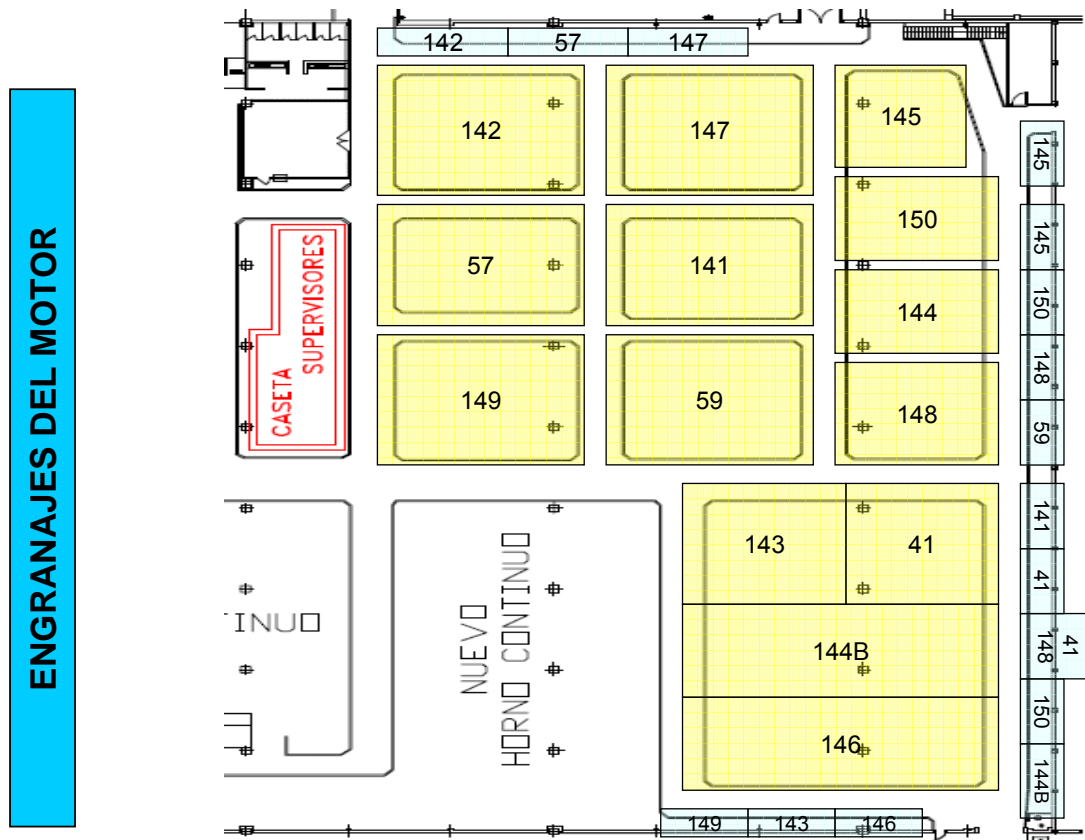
Sectorización de una parte de la Minifábrica de Ejes y Engranajes
